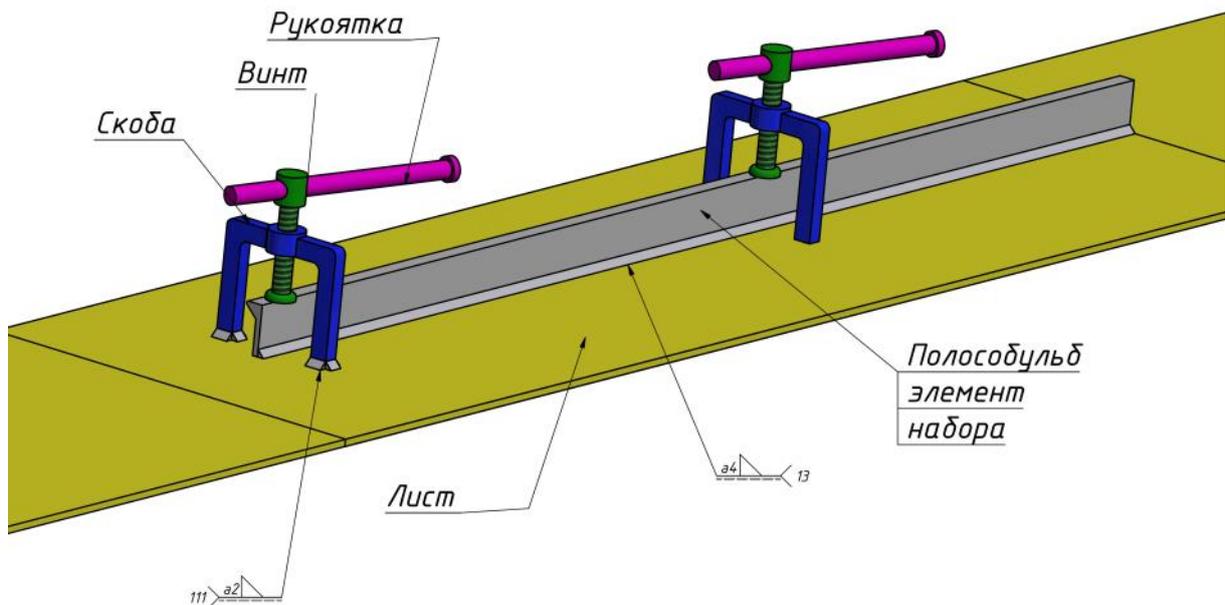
Применение прижима в виде П-образной винтовой скобы при сборке ребра набора к полотнищу под сварку. Рисунок автора.
